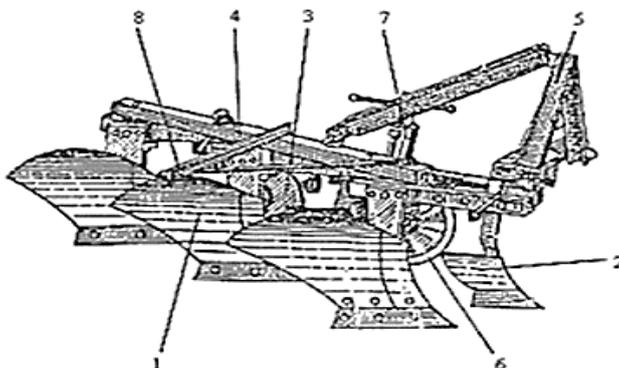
Навесной плуг ПЛН-3-35: 1 – корпус; 2 – предплужник; 3 – дисковый нож; 4 – рама; 5 – замок автосцепки; 6 – опорное колесо; 7 – винтовой механизм регулирования глубины пахоты; 8 – устройство для навески борок
